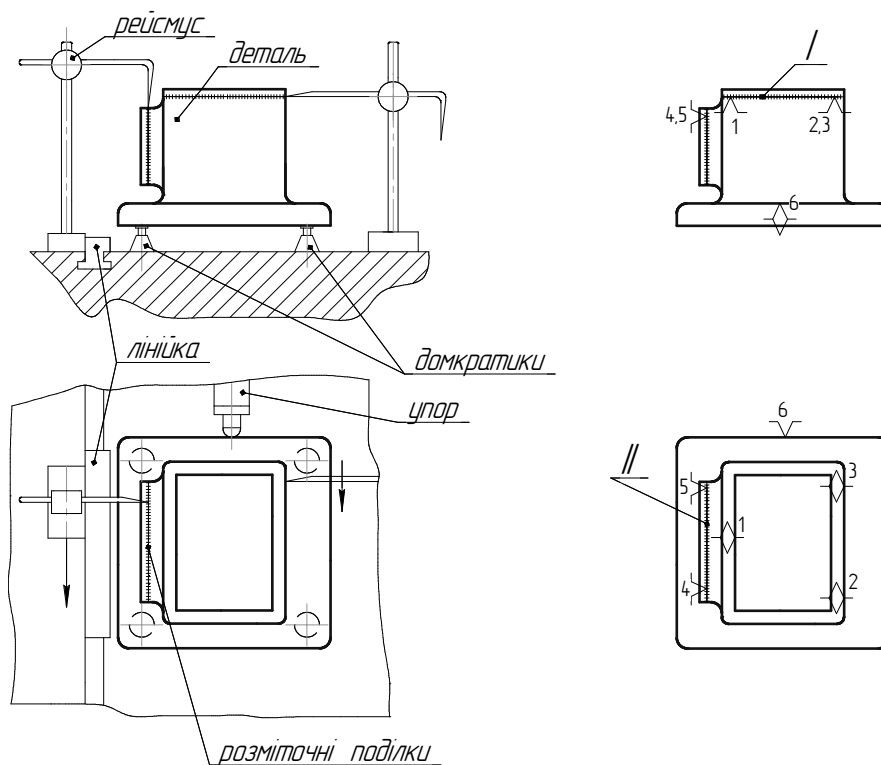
Схема базування корпусної деталі з вивірнянням її положення по розмічувальних рисках.
